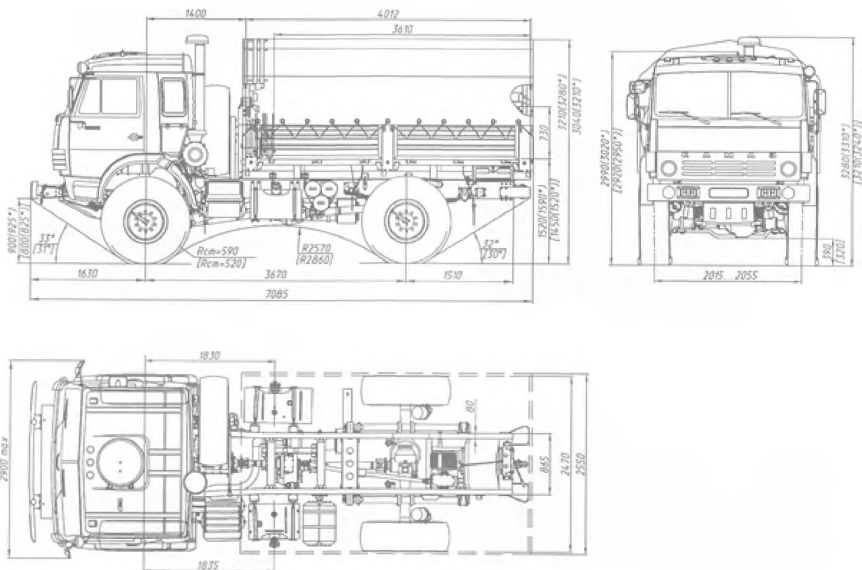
Автомобиль-тягач КАМАЗ-43501. Габаритные размеры для автомобиля с шинами КАМА-1260 (КАМА-430).
